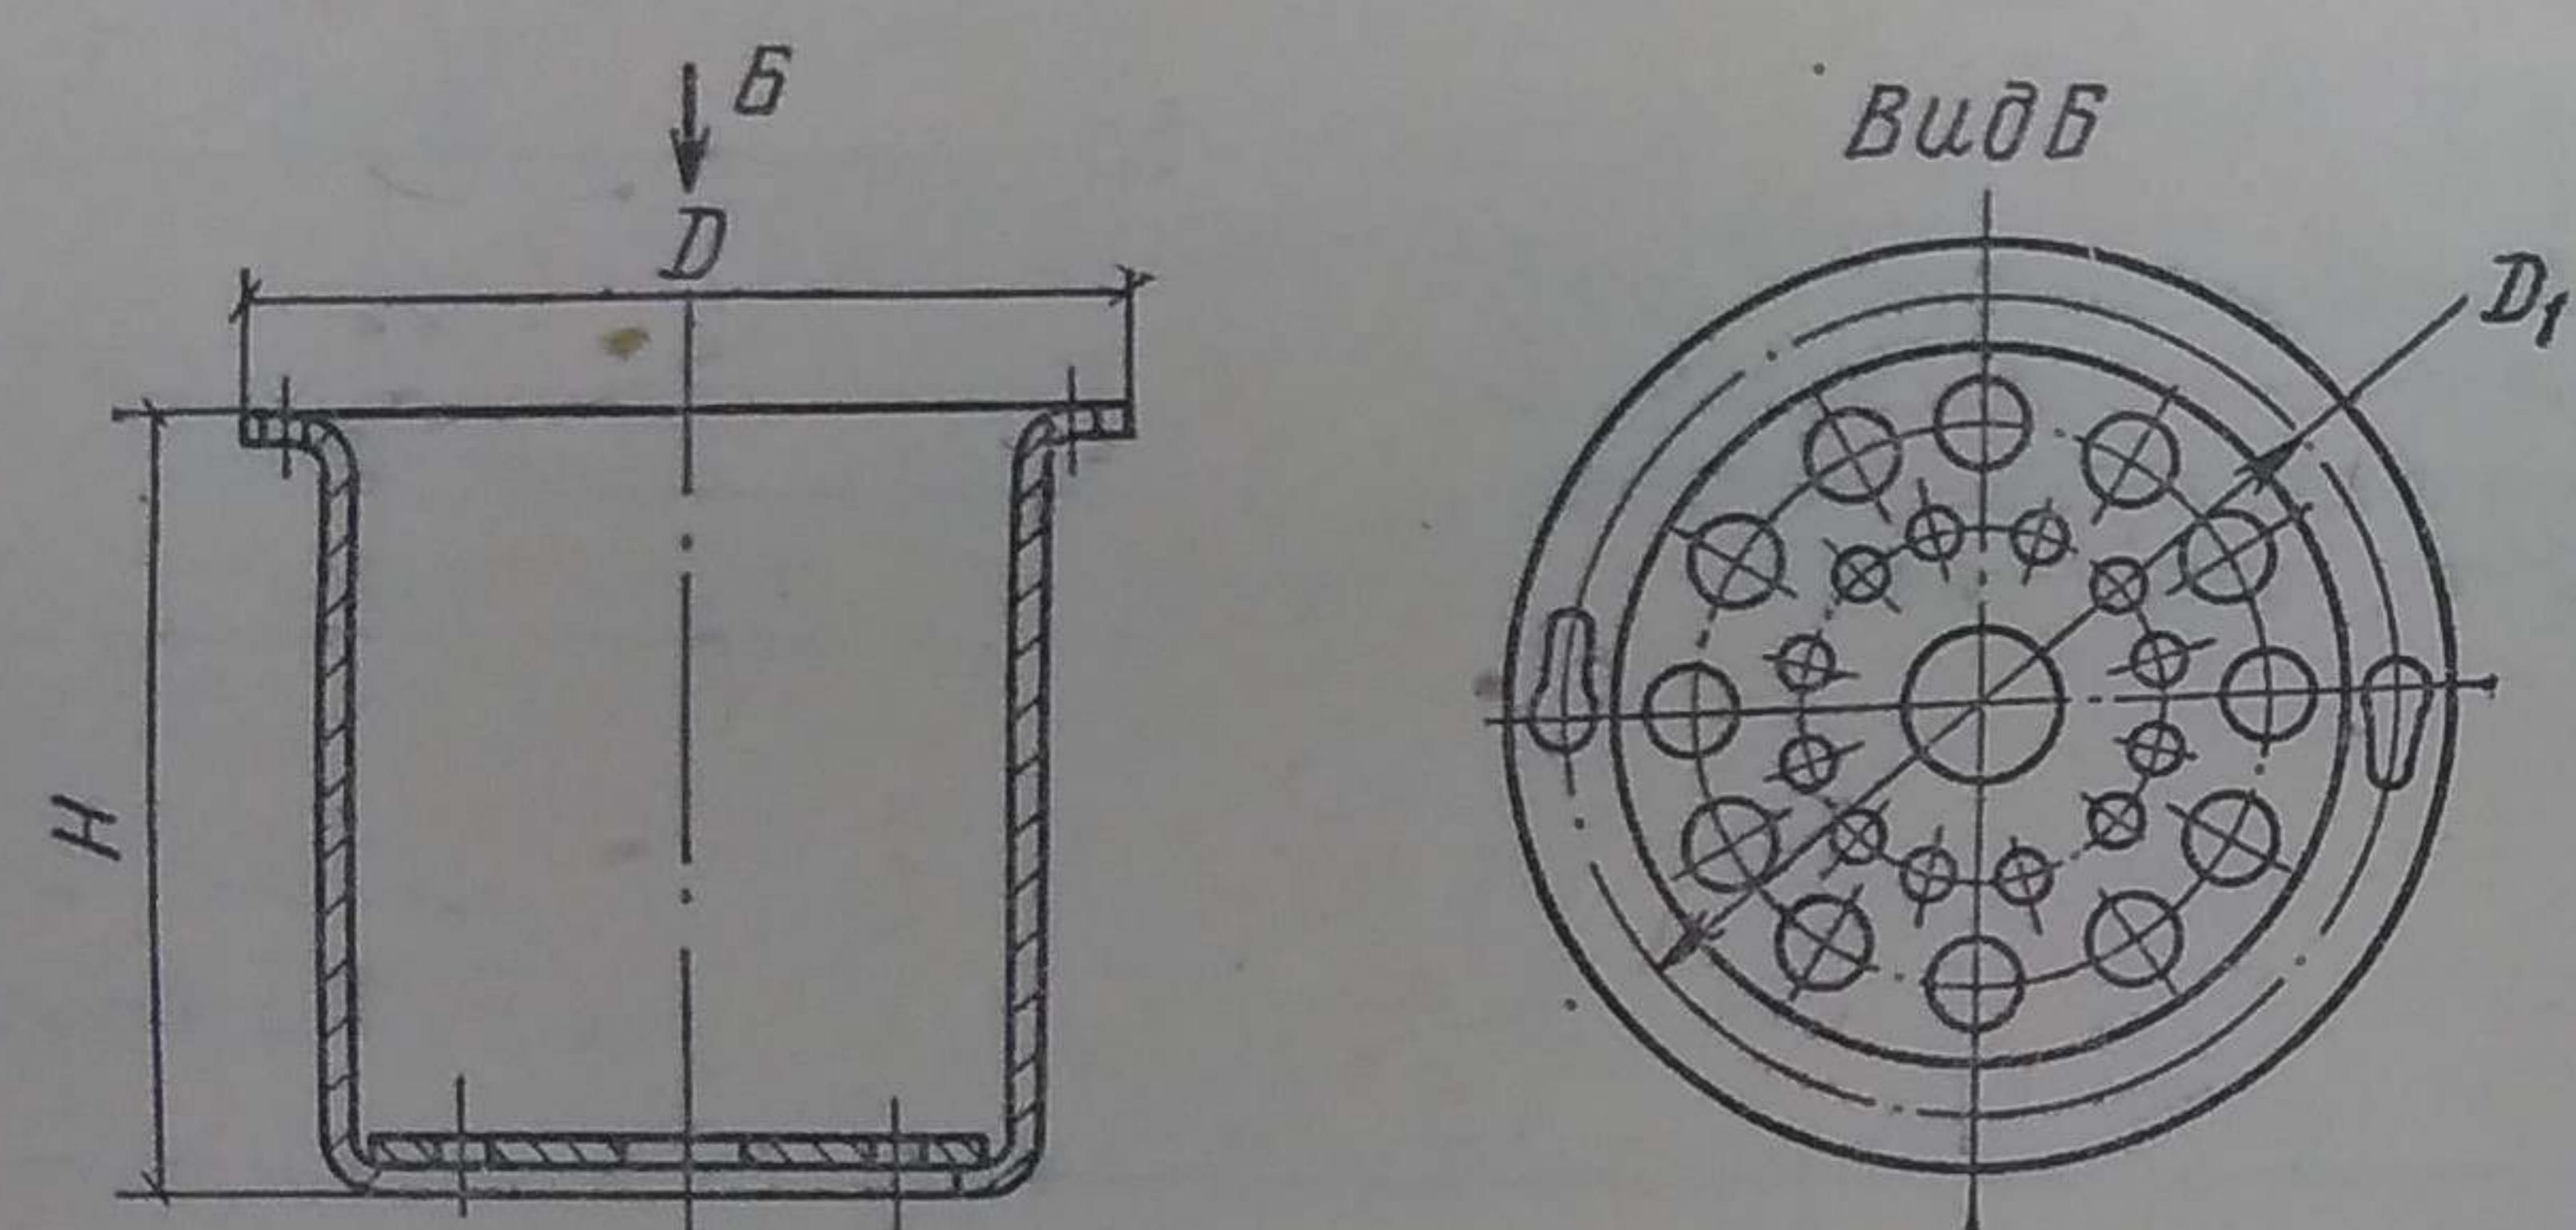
Маскировочное приспособление — затенитель-цилиндр для светильников внутреннего освещения
